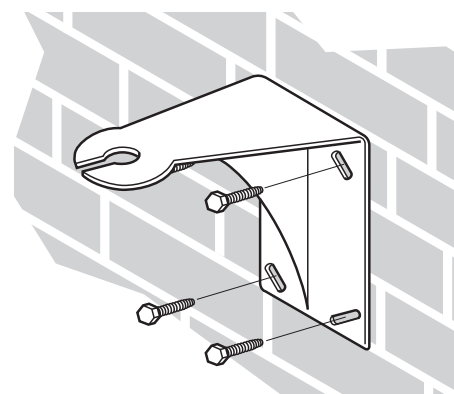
Fissaggio della staffa di montaggio LBB 3414/00 ad una parete
